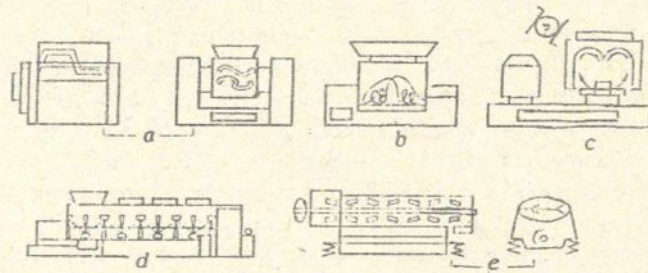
Malaxoare cu palete rotitoare de diferite forme: a — cu palete în formă de S; b — cu palete în formă de șurub; c — malaxor circular; d — tip șnec; e — vibromalaxor
